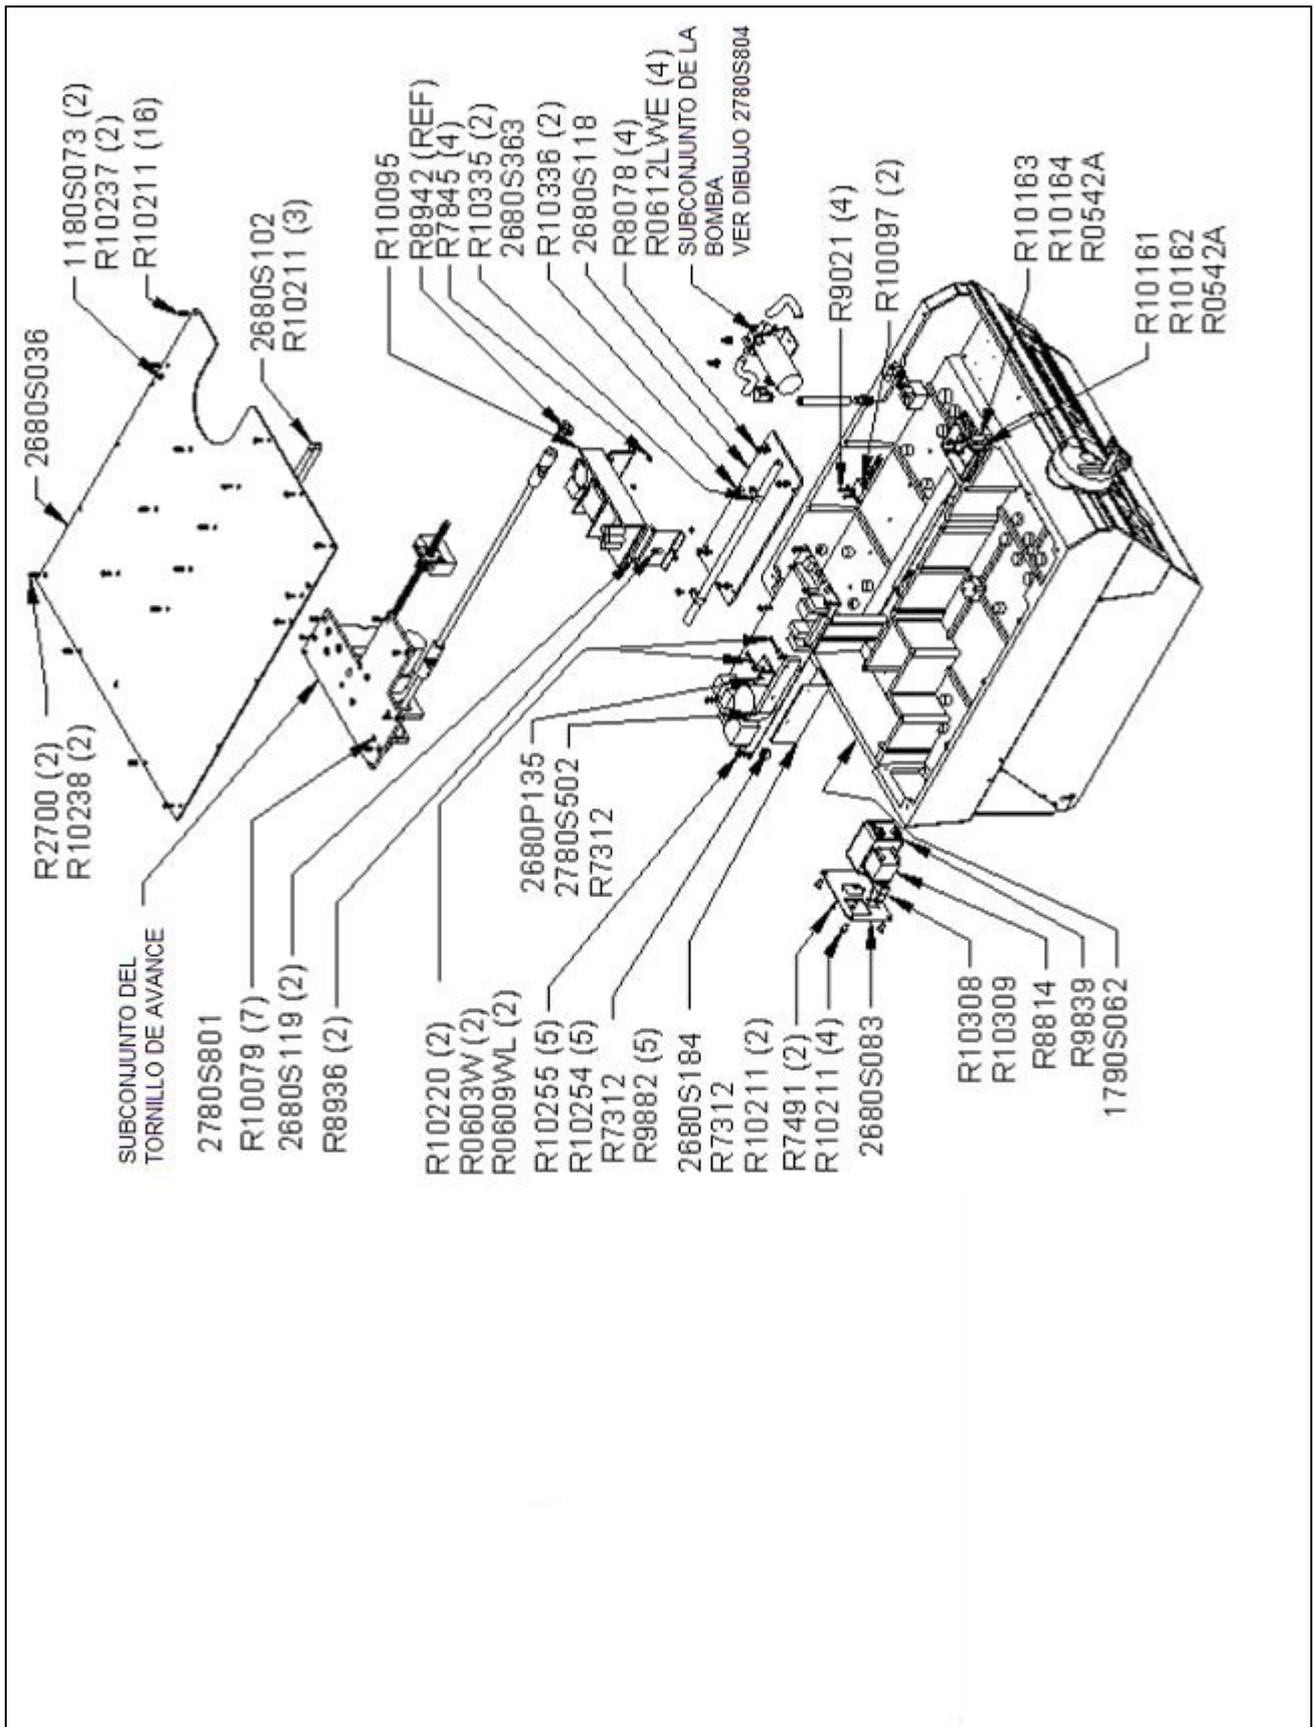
Dibujo de despiece de la IsoMet®5000, vista de la parte inferior (2780900C).
